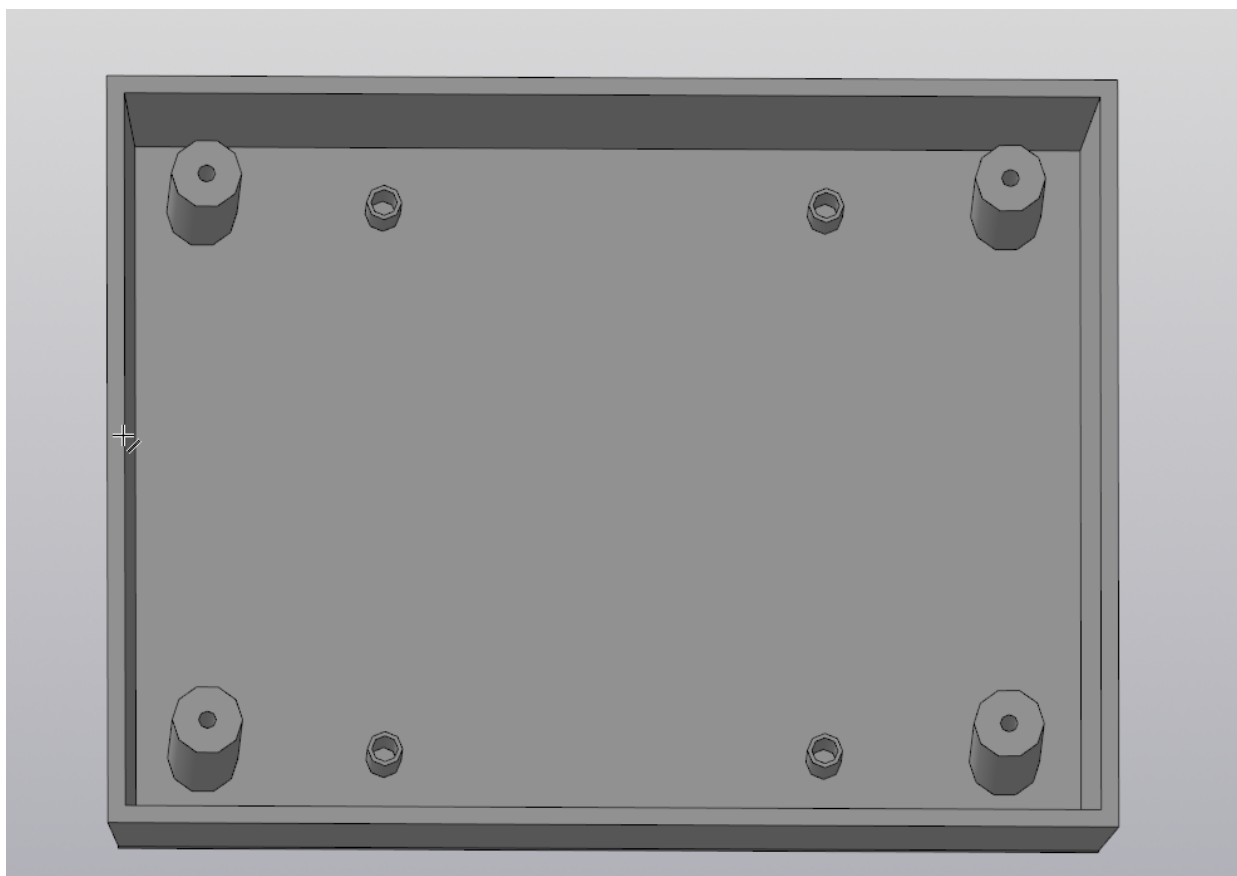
3D модель основания корпуса для установки электронной ячейки
